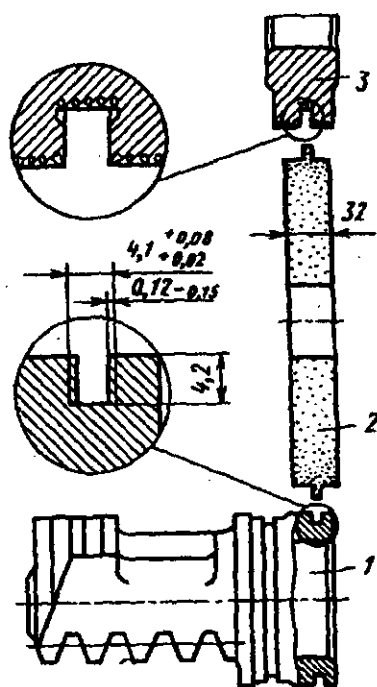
Схемы шлифования кольцевых канавок на поршне-рейке гидросилителя руля автомобиля ЗИЛ-130: 1 – шлифуемая деталь; 2 – шлифовальный круг; 3 – алмазный правящий ролик
